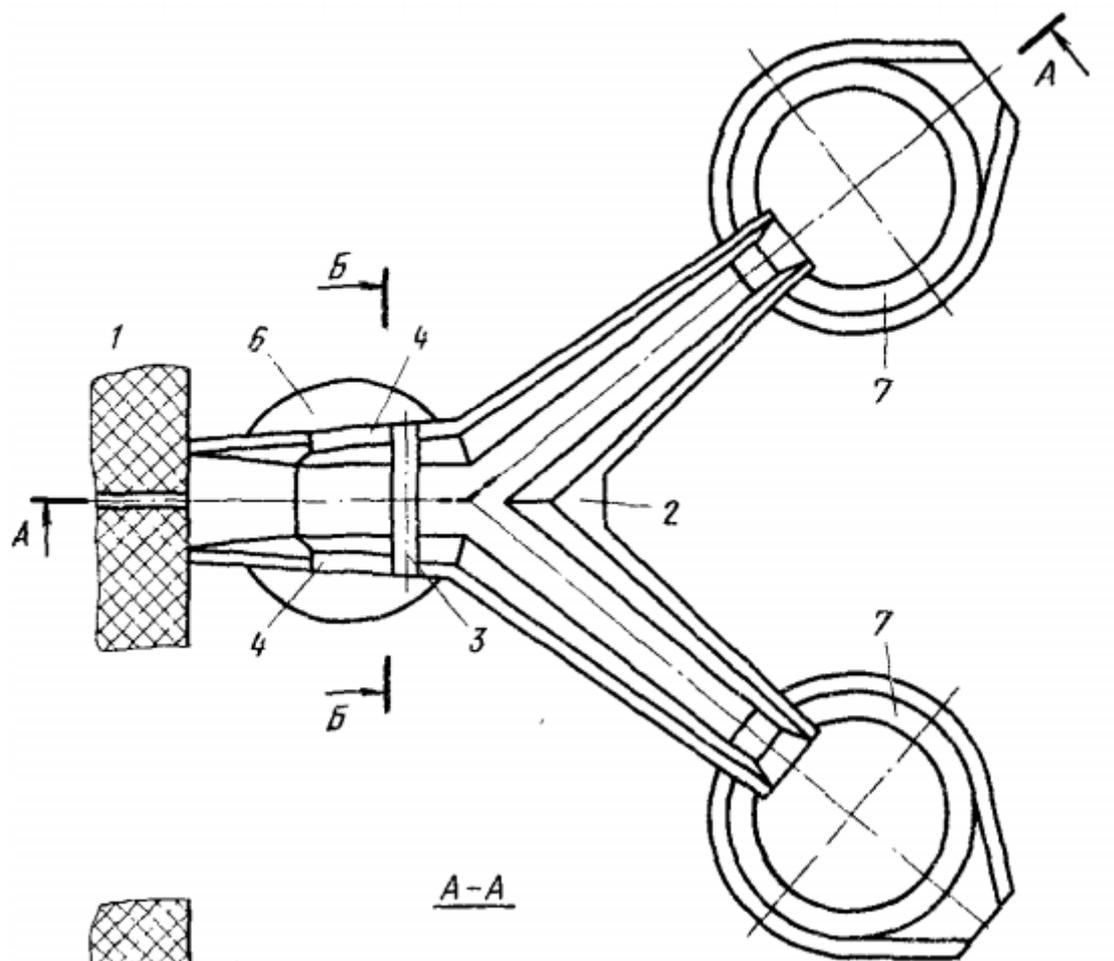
Схема двухручьевого универсального сталевыпускного желоба 1 — сталеплавильный агрегат; 2 — желоб; 3 — перегородка для отделения печного шлака; 4 — выем для слива шлака; 5 — механизм поворота желоба вокруг продольной оси; 6 — шлаковая чаша; 7 — сталеразливочный ковш
